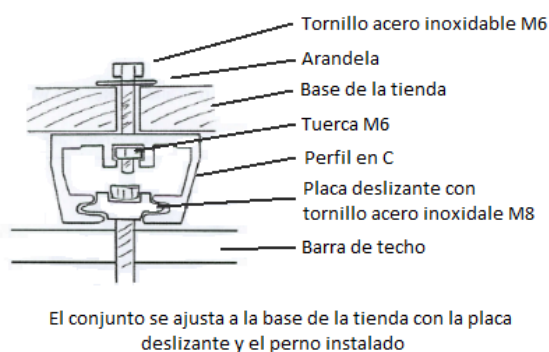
Vista en detalle y componentes de las fijaciones de techo. (Fuente: Propia)
